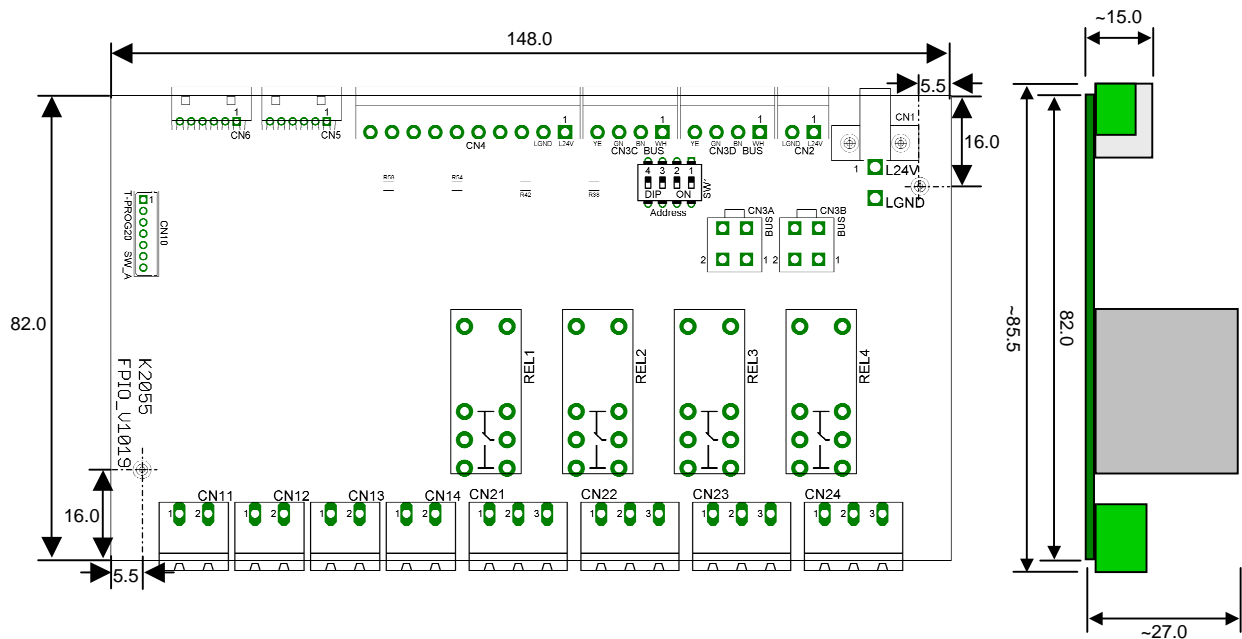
Abmessungen FPIO (Grundriss, Seitenriss)
